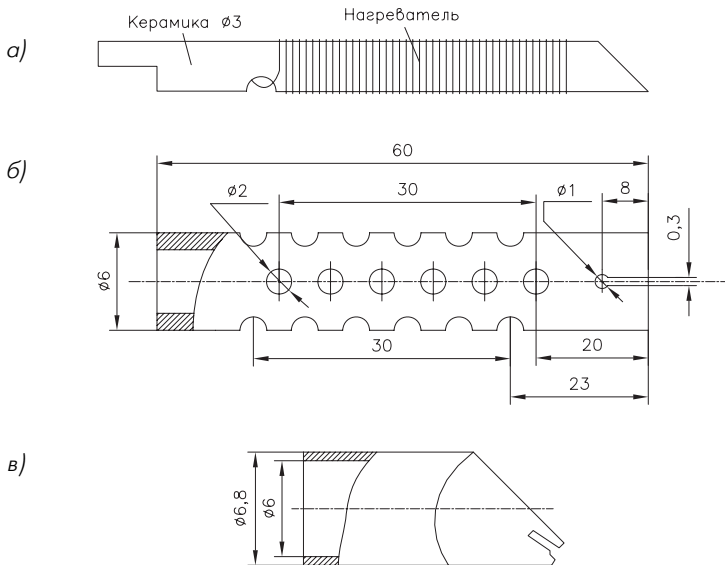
Основные детали микропаяльника для монтажа и демонтажа микросхем на печатные платы: керамический нагреватель (а), металлический защитный кожух (б), жало (в)
